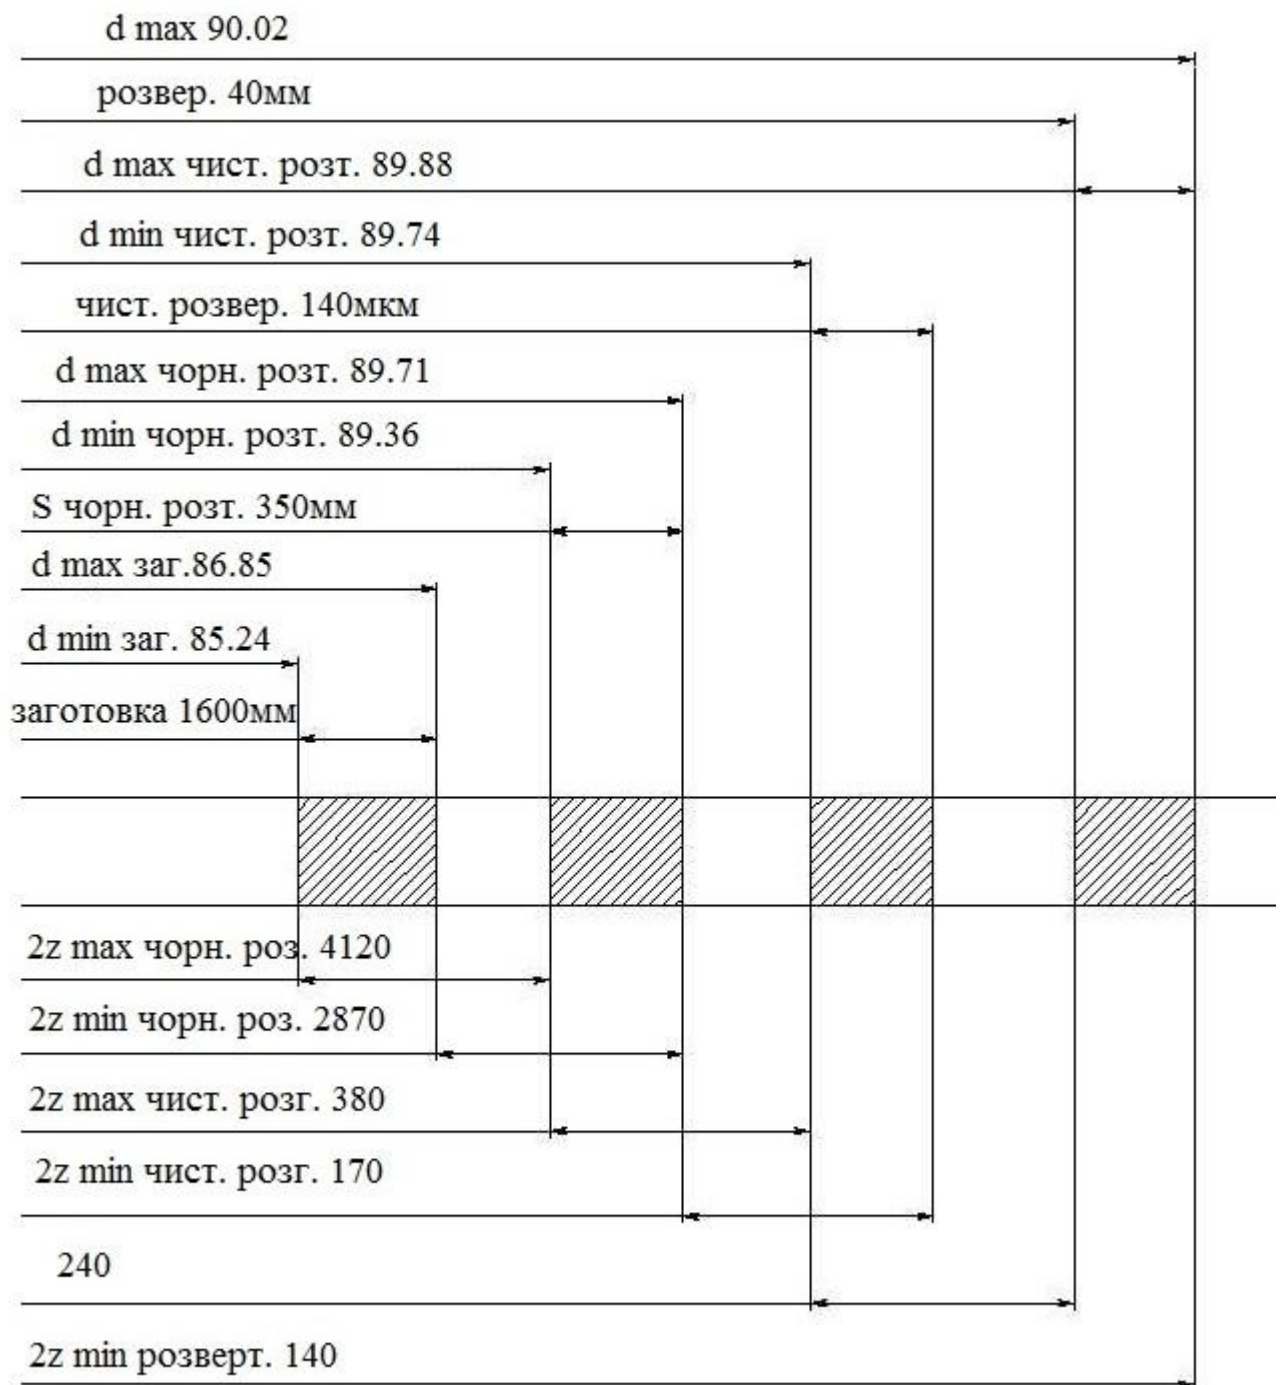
Схема графічного розмічування припусків і допусків на оброблення отворів $\varnothing 90_{-0.013}^{+0.022}$ корпусу механізму зворотного руху і роздаткової коробки.
